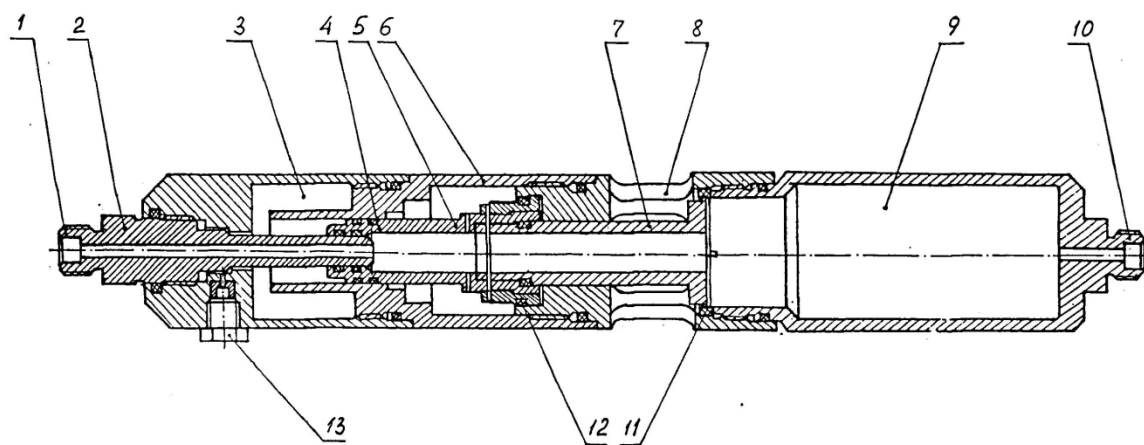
Пневмоизлучатель: 1, 10 – штуцер; 2 – золотник; 3 – полость демпферная; 4 – поршень; 5 – хвостовик; 6 – переходник; 7 – поршень двухфланцевый; 8 – окно; 9 – ресивер; 11, 12 – уплотнительные кольца; 13 – заглушка
